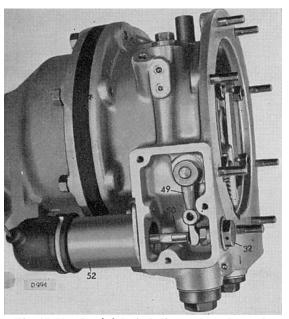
Vue du côté droit de l'ensemble, plaque de solénoïde retirée
